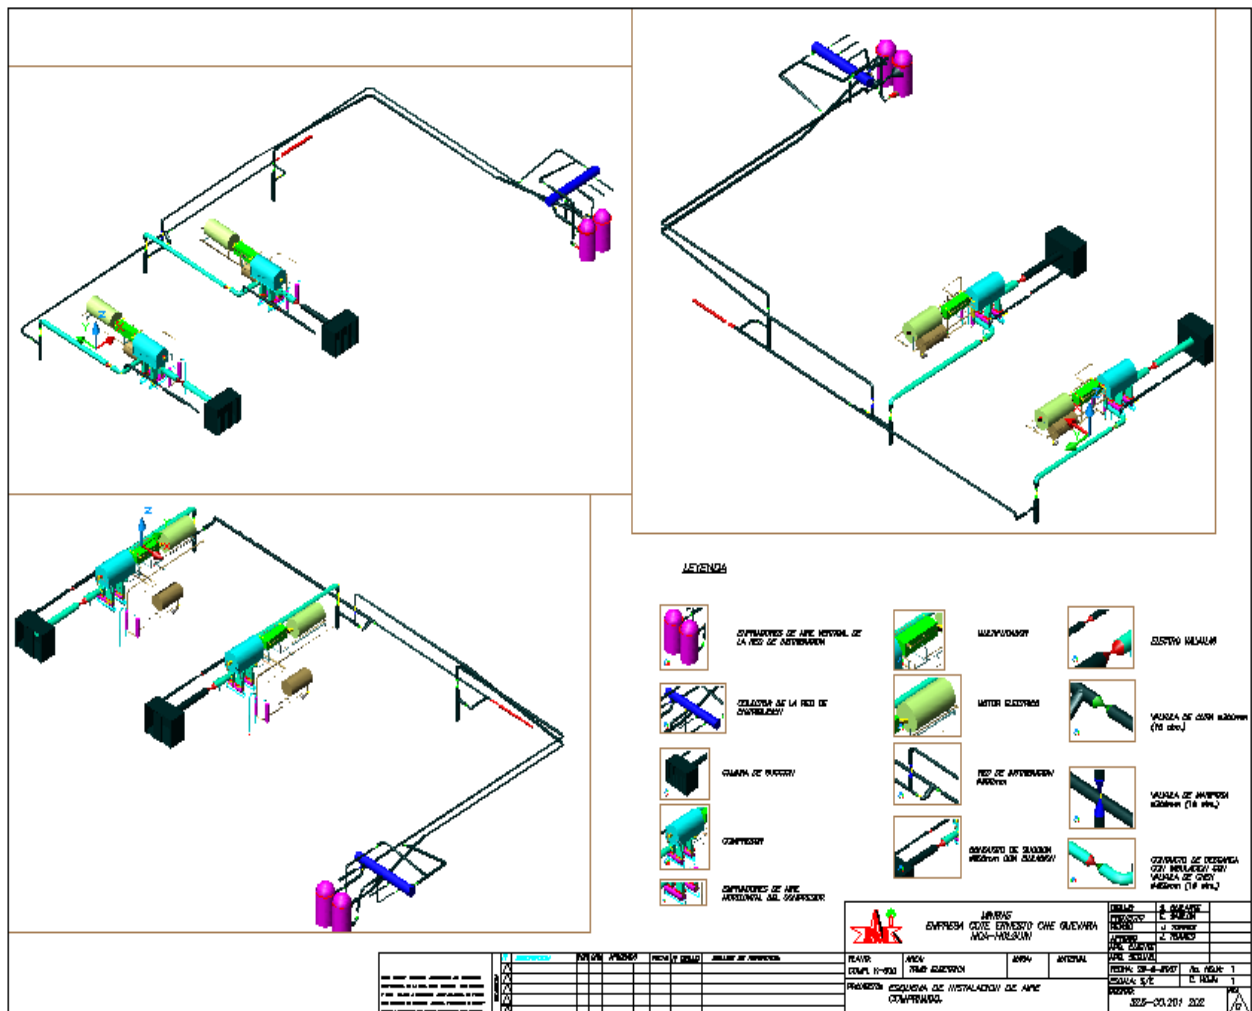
Vistas de la instalación de aire comprimido del conjunto motor, Multiplicador, compresor y sistema de lubricación en 3ra. dimensión.
